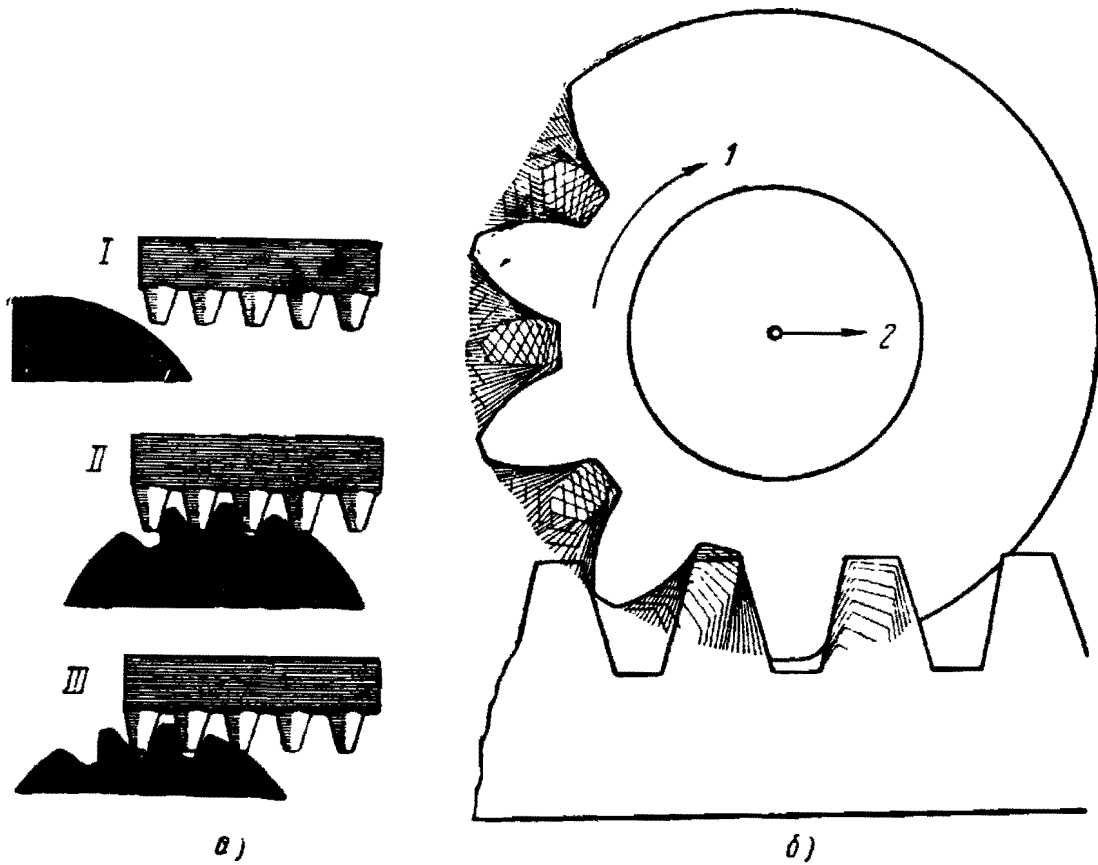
Схемы нарезания зубчатого колеса гребенкой на станке типа Маар:
